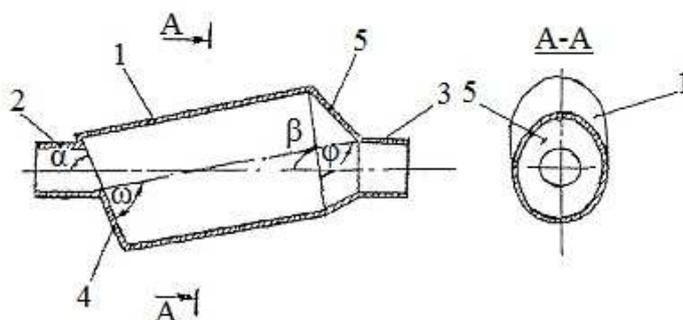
Рабочий орган устройства для приготовления кормов:
